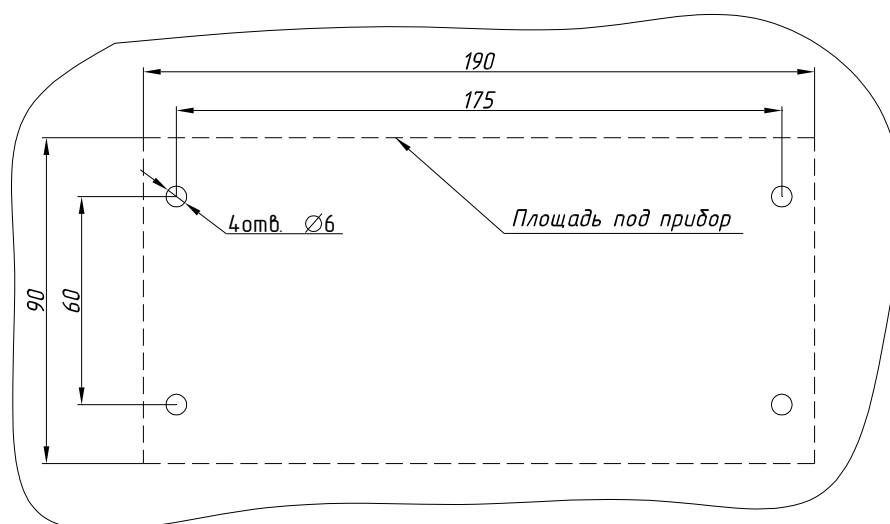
Посадочные размеры для прибора Ф1791.2
